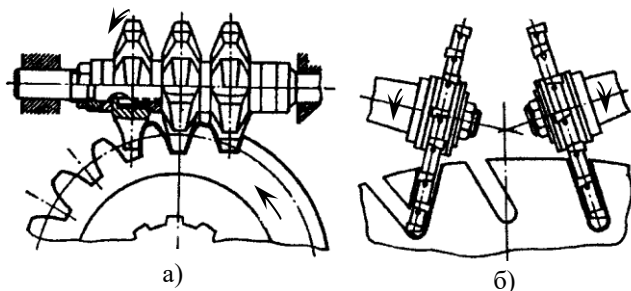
Нарізання зубів зубчастих коліс дисковими фрезами:
